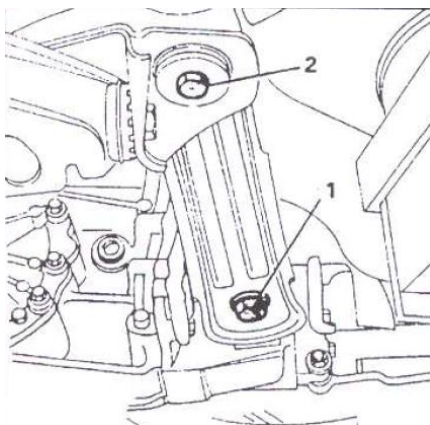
PERNOS DE MOTOR DE ARRANQUE
